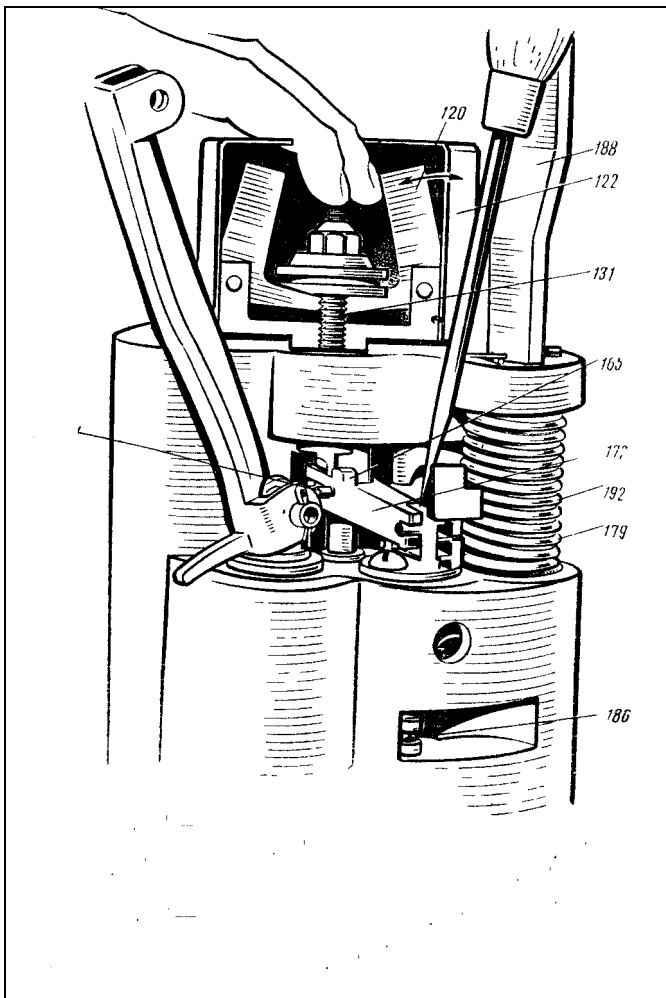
120 — муфта регулятора с встроенным упорным подшипником; 122 — груз регулятора; 131 — шток; 165—распределительный золотник; 170—палец золотника и плавающей рычага; 171— шплинт; 172 — плавающий рычаг; 179 — наконечник штока принимающего поршня; 188—штанга задающего поршня изодрома; 192—задающий поршень изодрома
